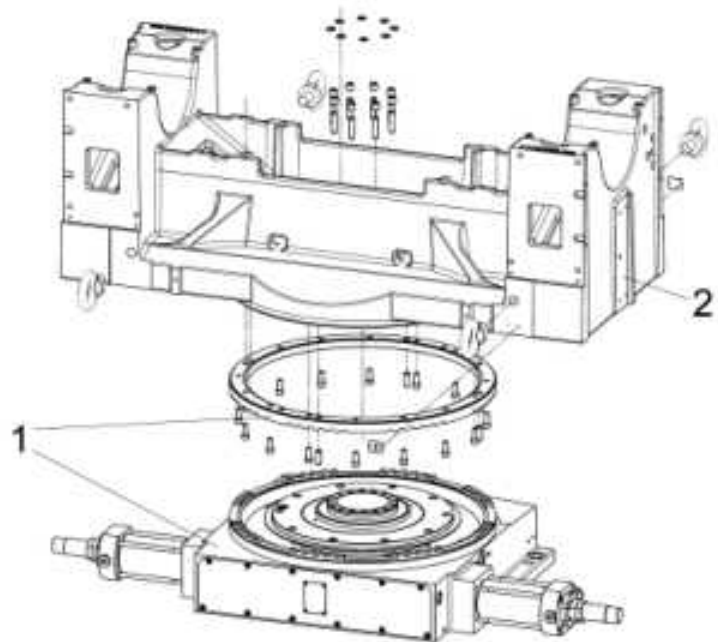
Schema Explosion-Zeichnung, Werkstückwechsler Zusammenbau
